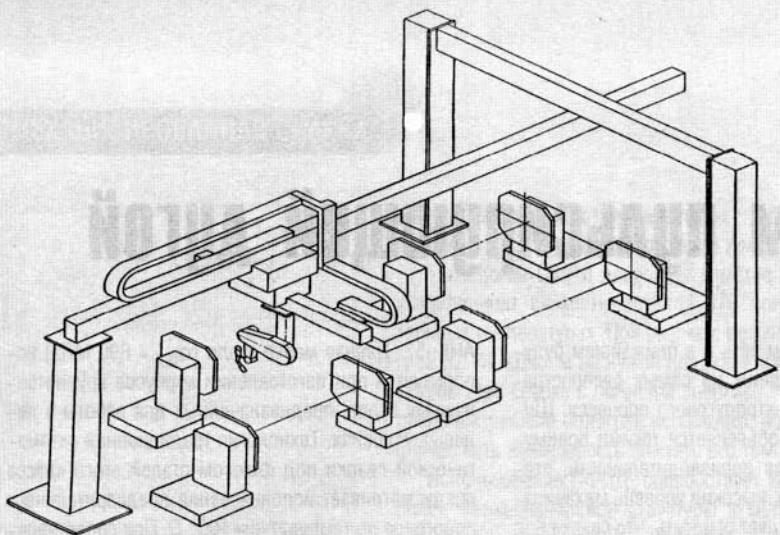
Робототехнологический комплекс для дуговой сварки в среде CO₂ крупногабаритных рамных конструкций
